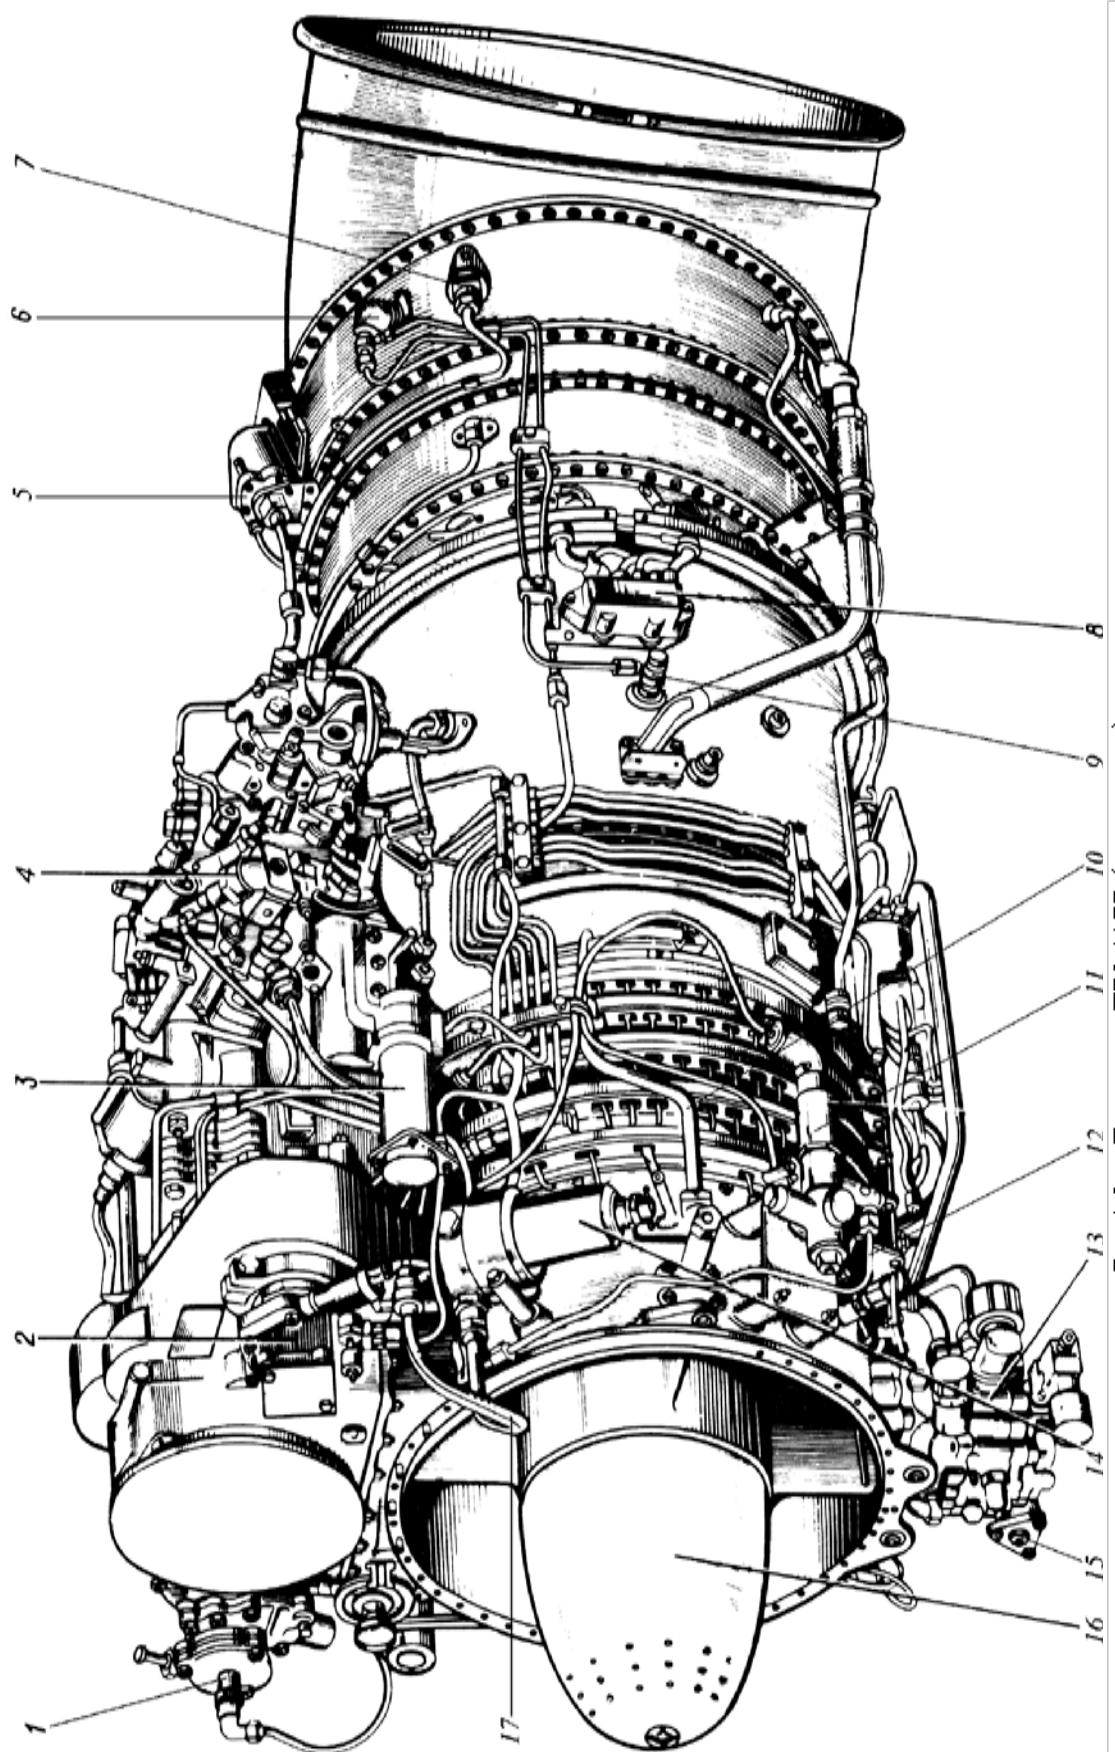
Двигатель ТВЗ-117В (вид справа):
